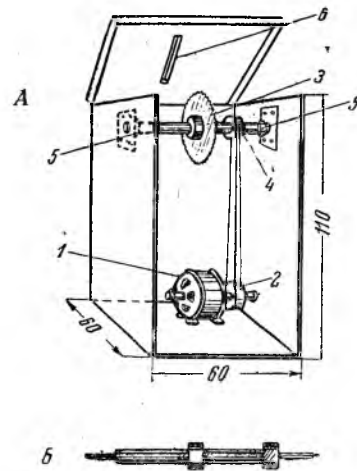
Циркулярная пила. А — деревянный ящик, в котором смонтирована пила: 1 — электромотор; 2 — деревянный шкив; 3 — диск пилы; 4 — второй деревянный шкив; 5 — шарикоподшипники; 6 — прорез в крышке ящика. Б — валик, на который насаживается диск пилы
